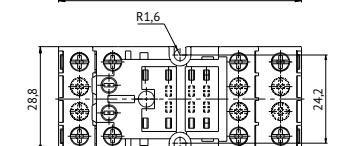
Габаритные, установочные, присоединительные размеры розеток OptiRel G RR94-7X
